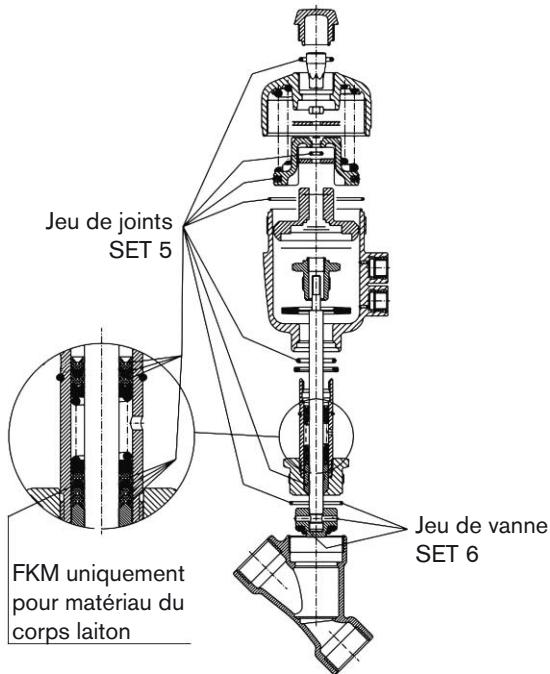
Pièces de rechange pour vanne à siège incliné
